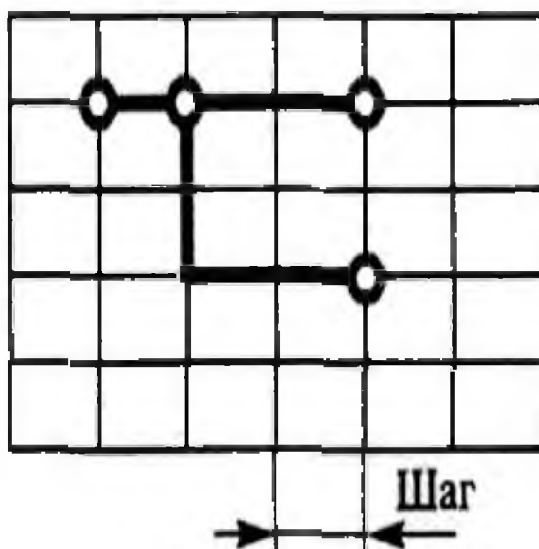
Координатная сетка чертежа печатной платы.
